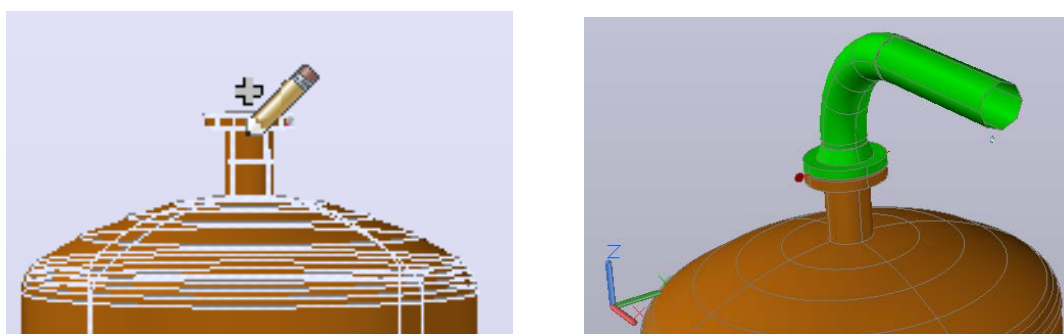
Zařízení (Equipments) výkres CV-9001-E3D-001.dwg
